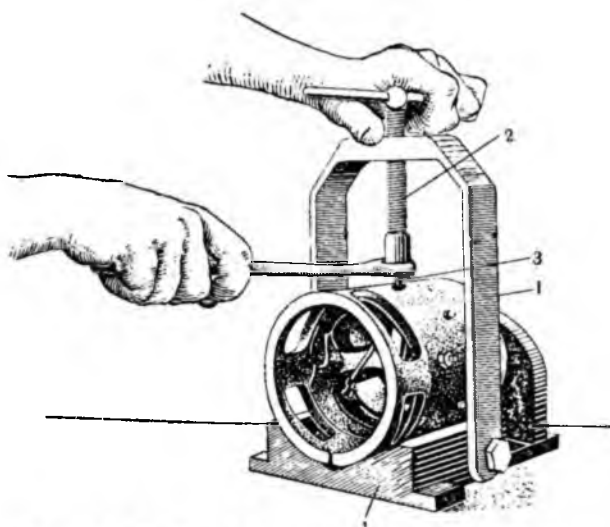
Разборка корпуса генератора ГБТ-4541.
